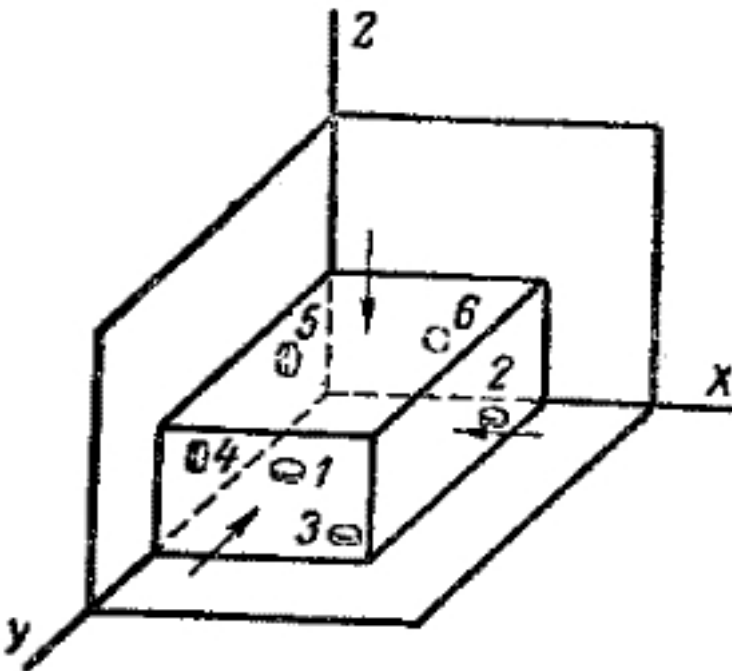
Схема установки деталей призматической формы по правилу шести точек.
